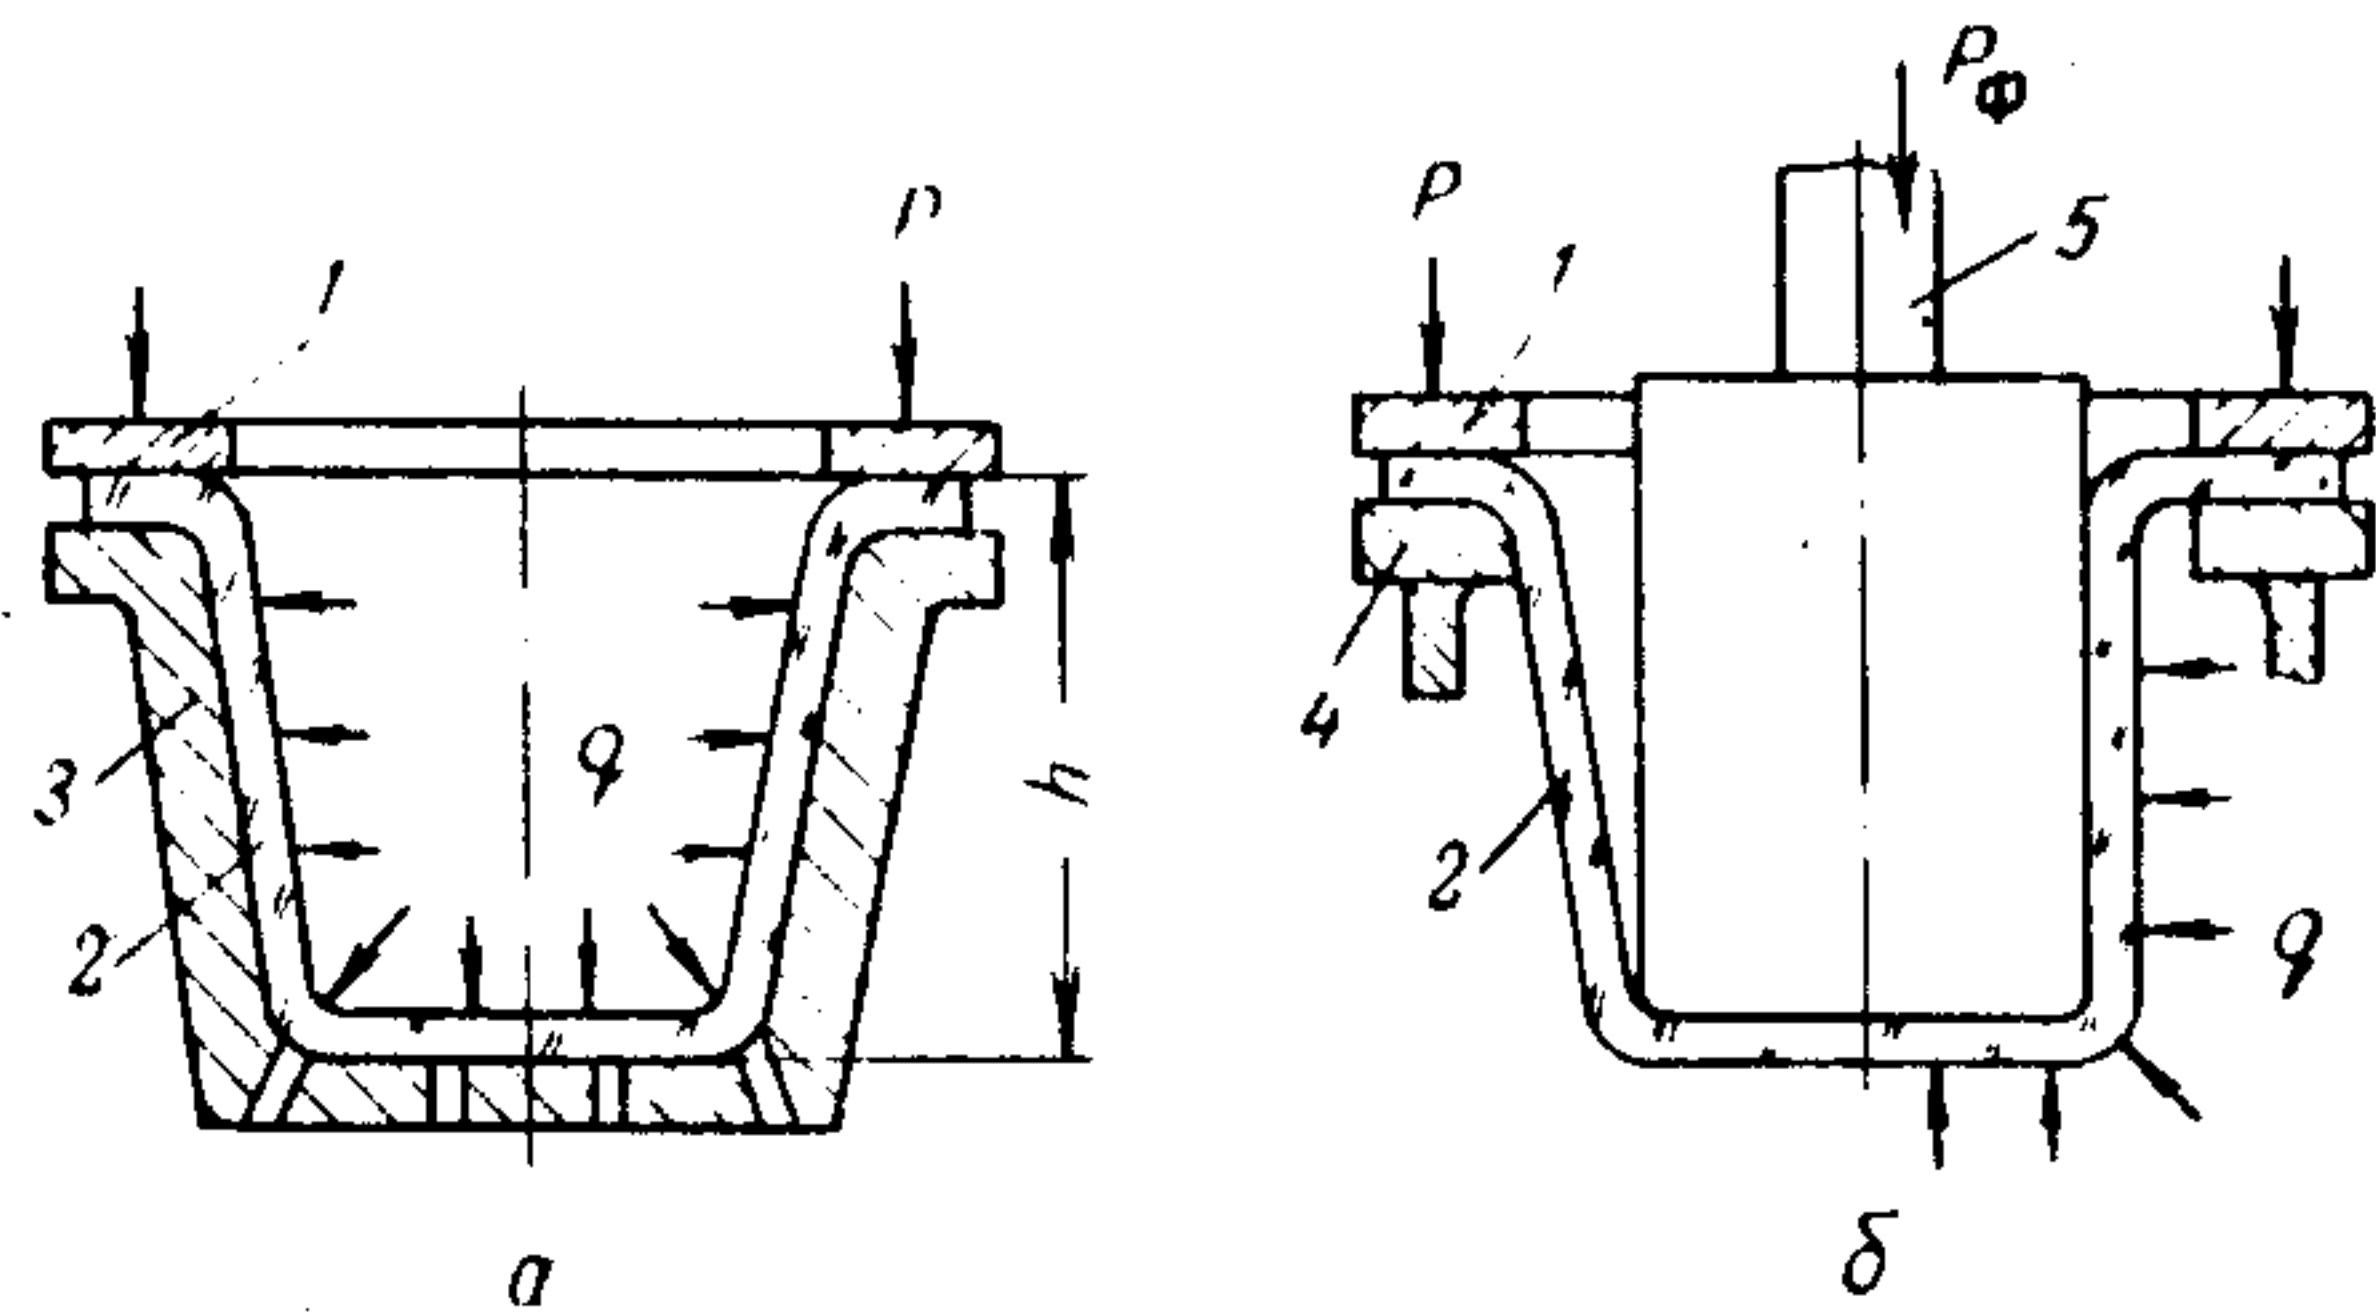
Схема вакуумной штамповки в негативную форму (а) и механошневматической штамповки (б): 1 — прижимное кольцо; 2 — заготовка; 3 — матрица; 4 — протяжное кольцо; 5 — пуансон.
